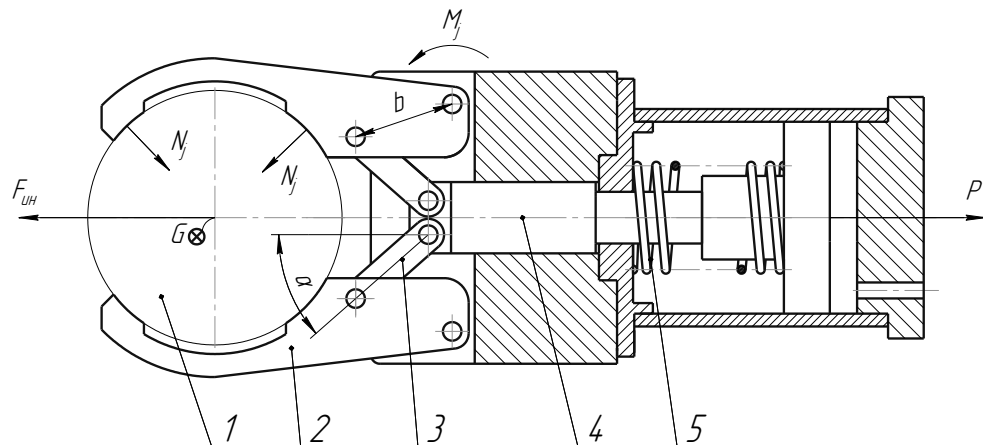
Розрахункова схема схвата: 1 – заготовка; 2 – губка схвата; 3 – важіль; 4 – повзун; 5 – затискна пружина
